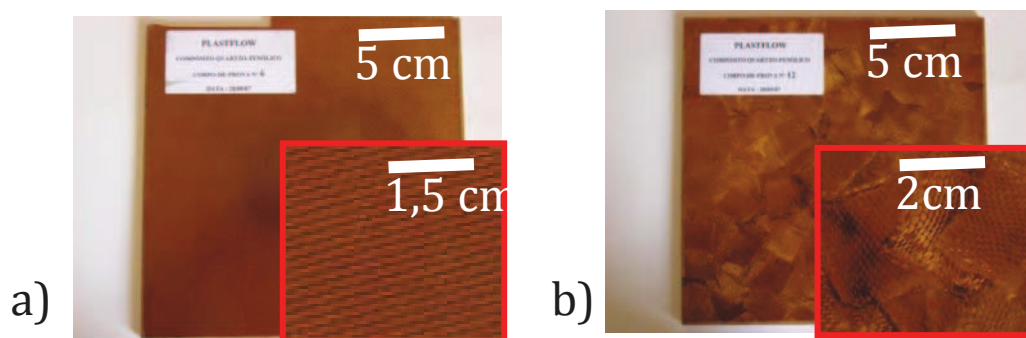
a) Plaque régulière, b) Plaque « irrégulière »
